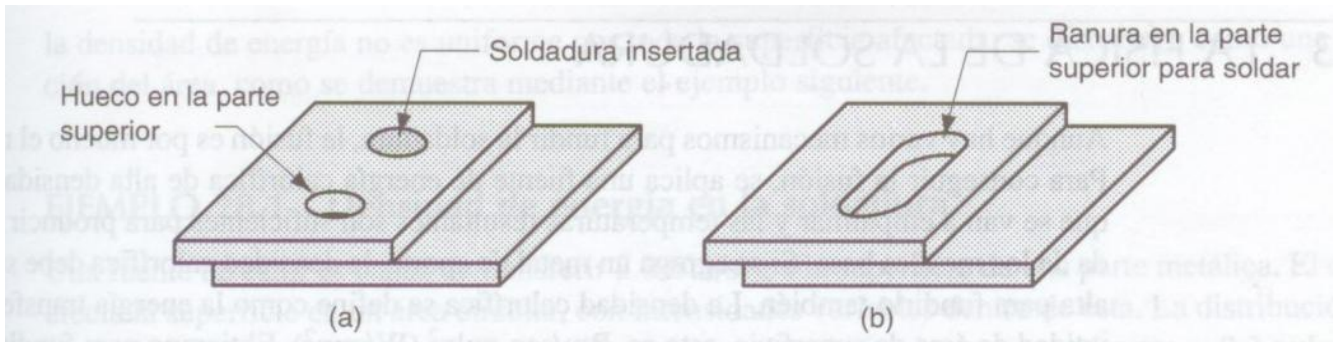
(a) Soldadura con inserto y (b) soldadura en ranura.
